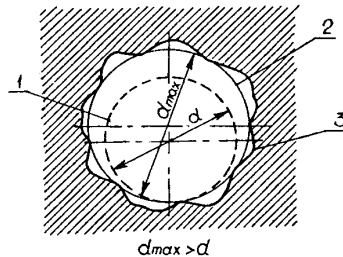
Прилегле коло для внутрішніх поверхонь обертання
